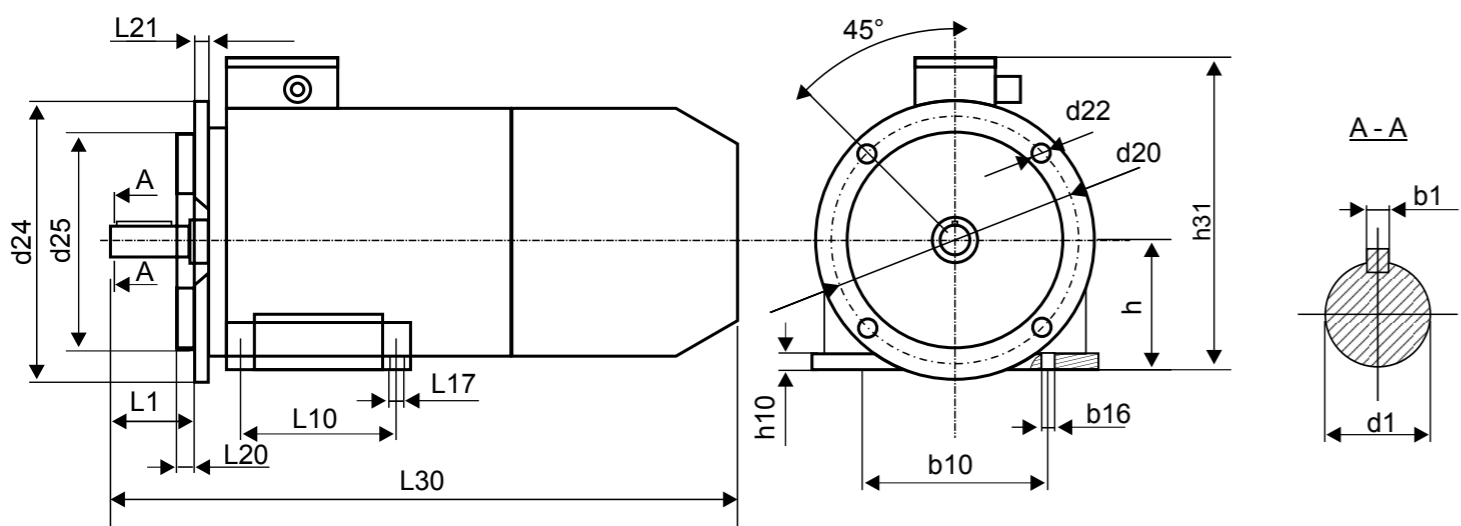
Габаритные и установочно-присоединительные размеры (IM2001)
